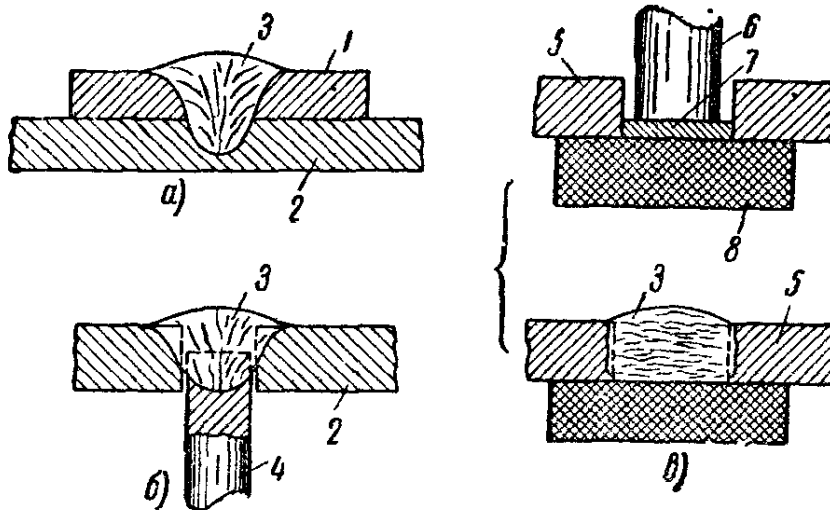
Разные случаи сварки электрозаклепками:
